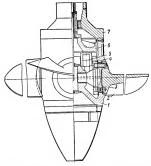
Рабочее колесо поворотнолопастной турбины без штока и крестовины. 1- втулка; 2- рабочая лопасть; 3- цапфа; 4- рычаг; 5- серьга; 6- поршень сервомотора; 7- вал турбины.
